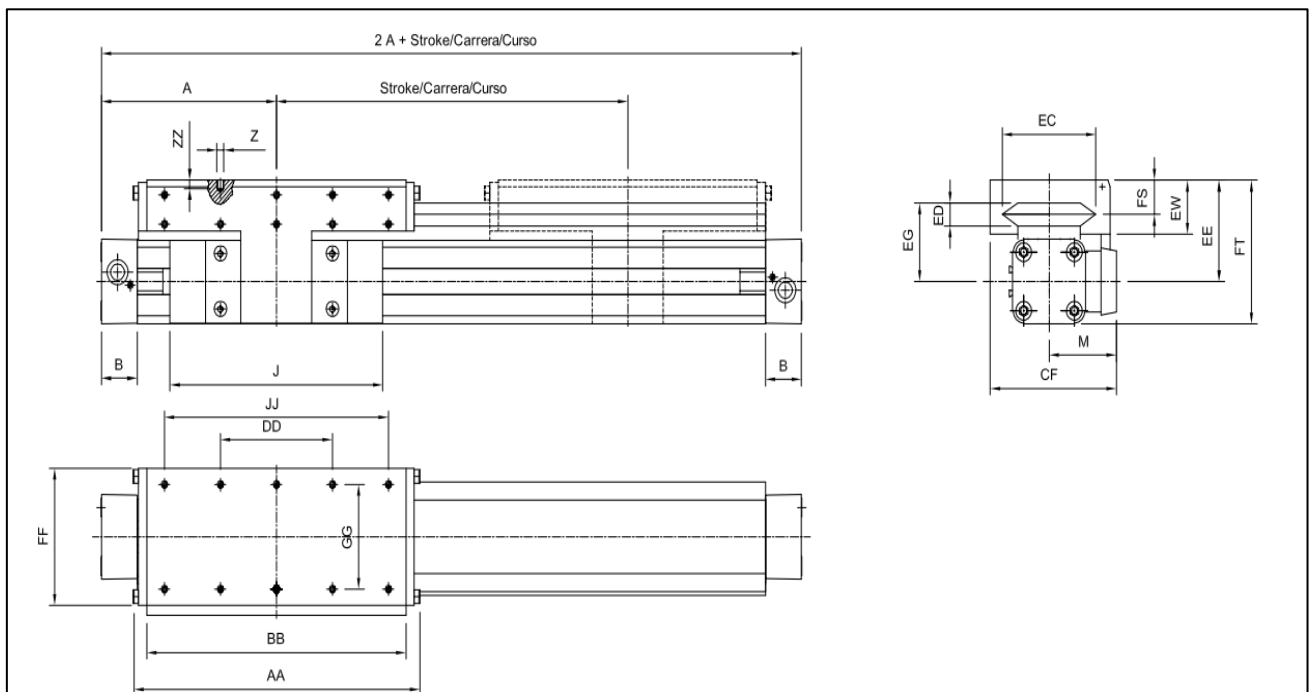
Desenho com as principais dimensões do cilindro sem haste [20]
